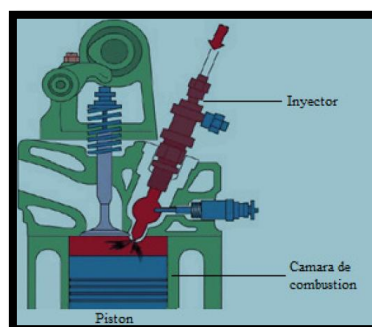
Descripción de la cámara de inyección directa de un motor diésel
